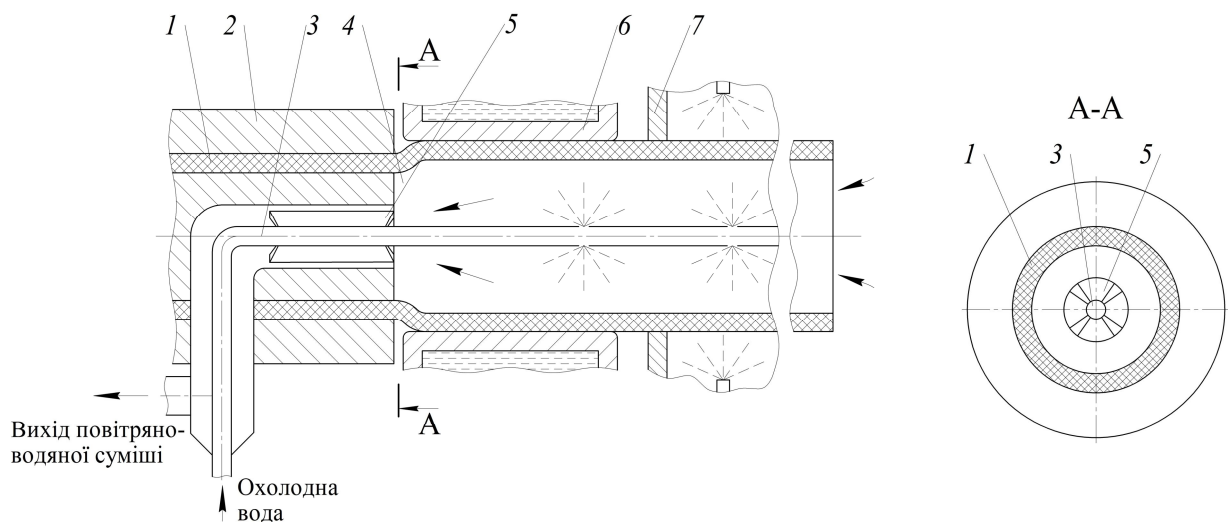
Схема пристрою безперервного формування полімерних труб: 1 – труба; 2 – трубна головка; 3 – трубчастий елемент; 4 – внутрішній простір труби; 5 – канал; 6 – калібрувальний пристрій; 7 – ванна
